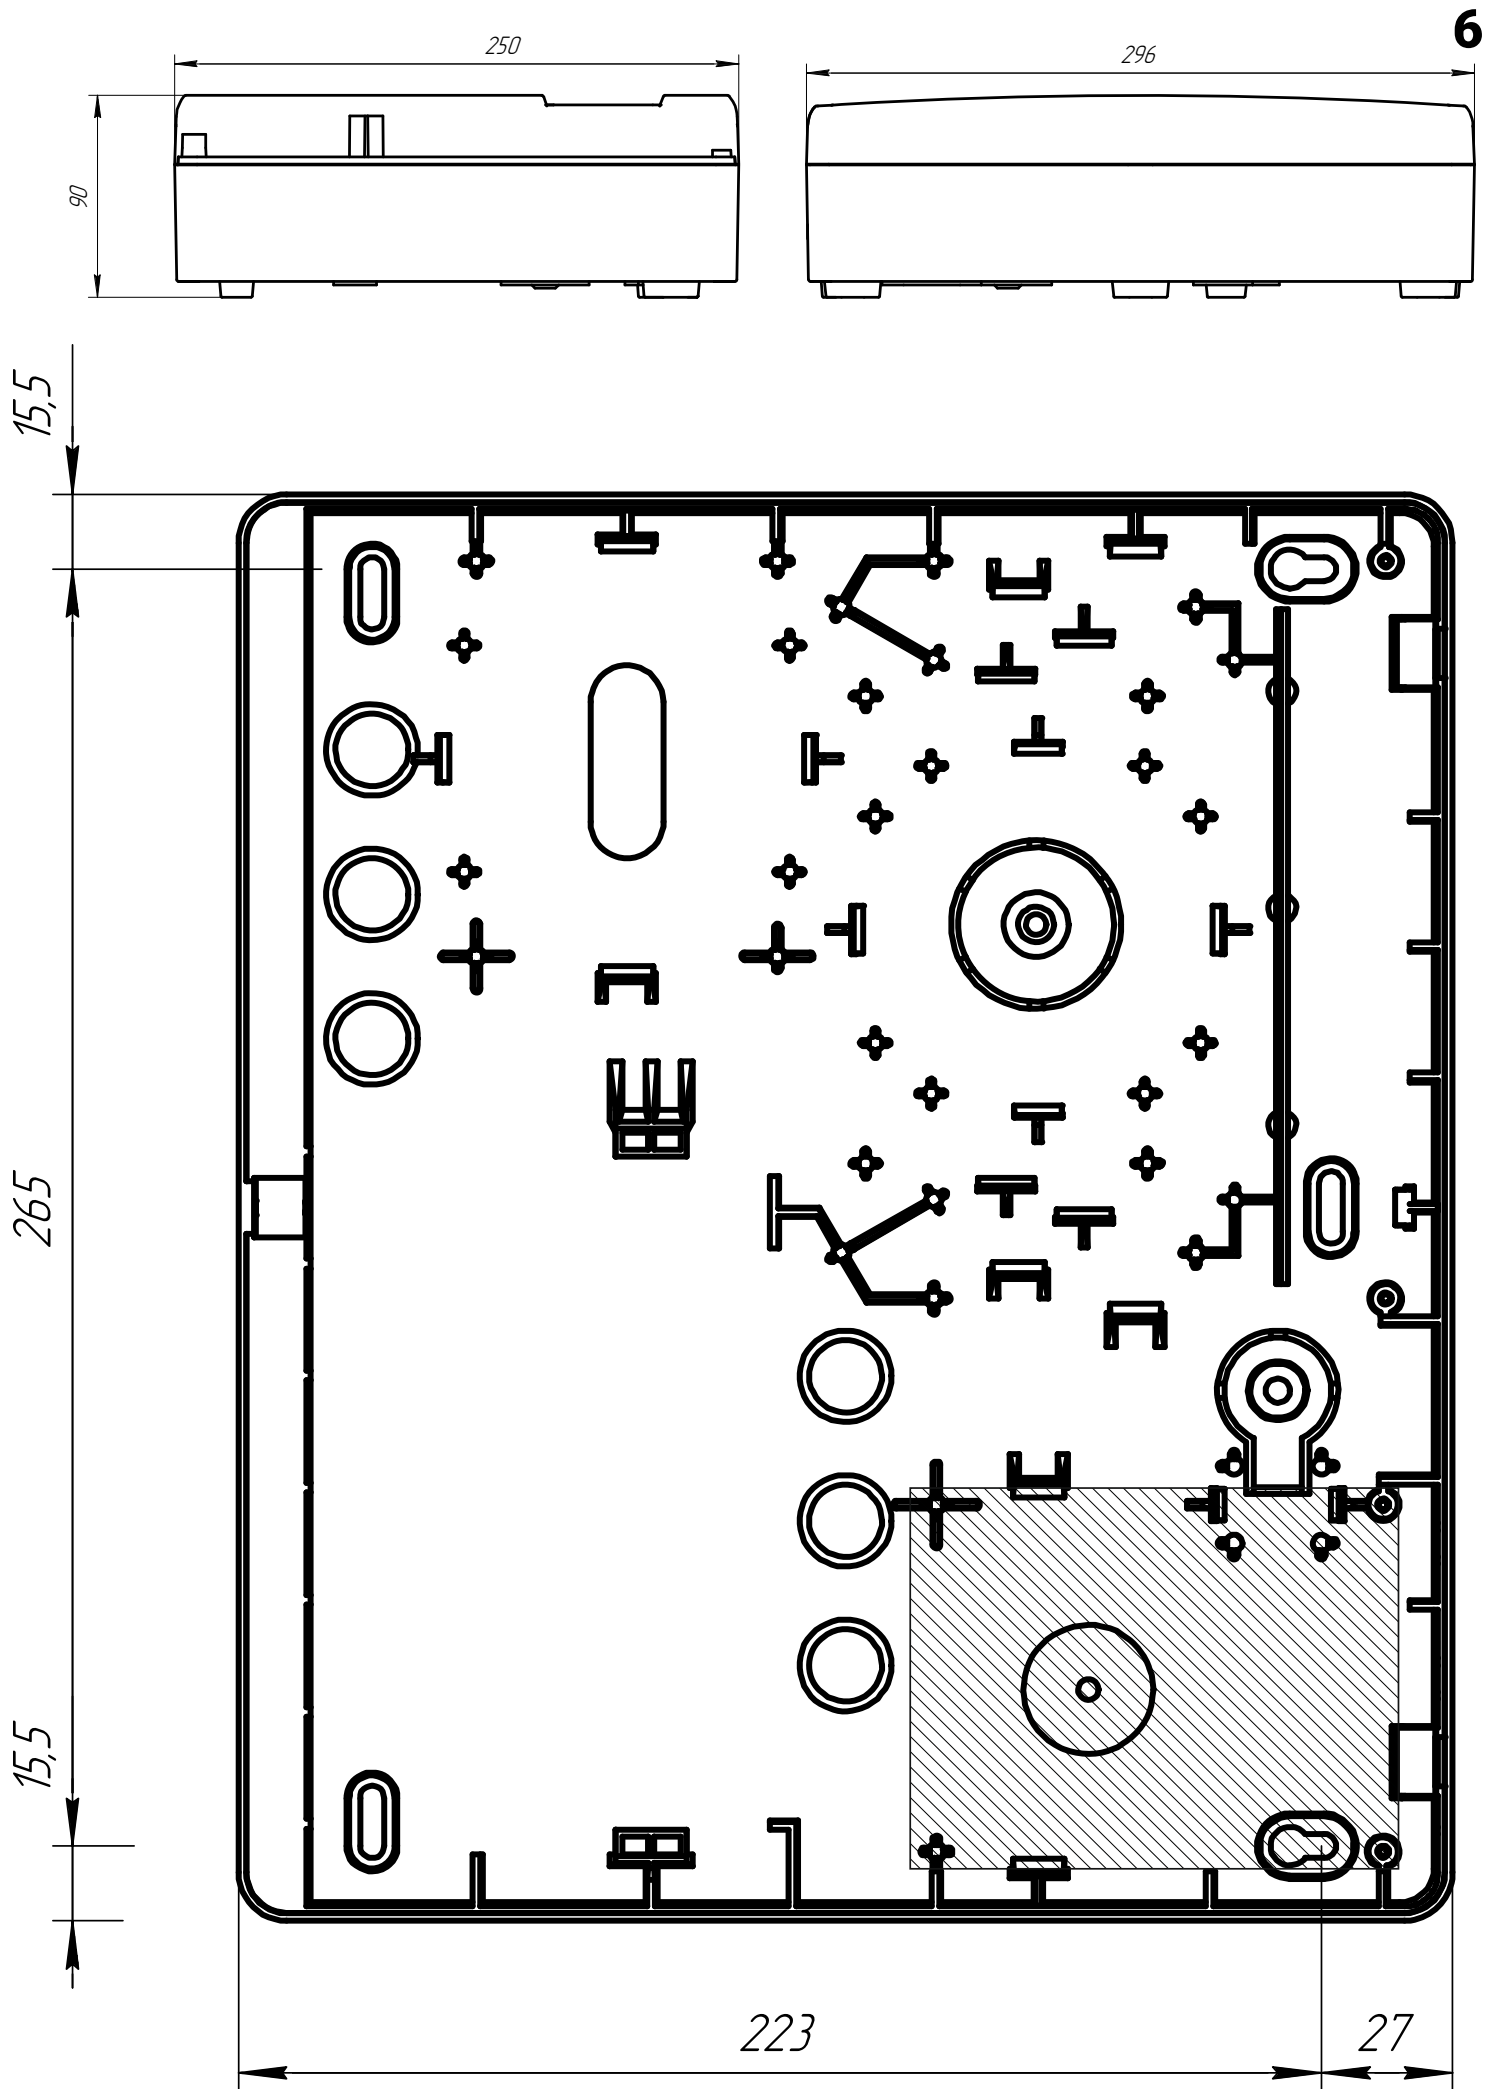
Корпус «Контакт» под АКБ 7 Ач
